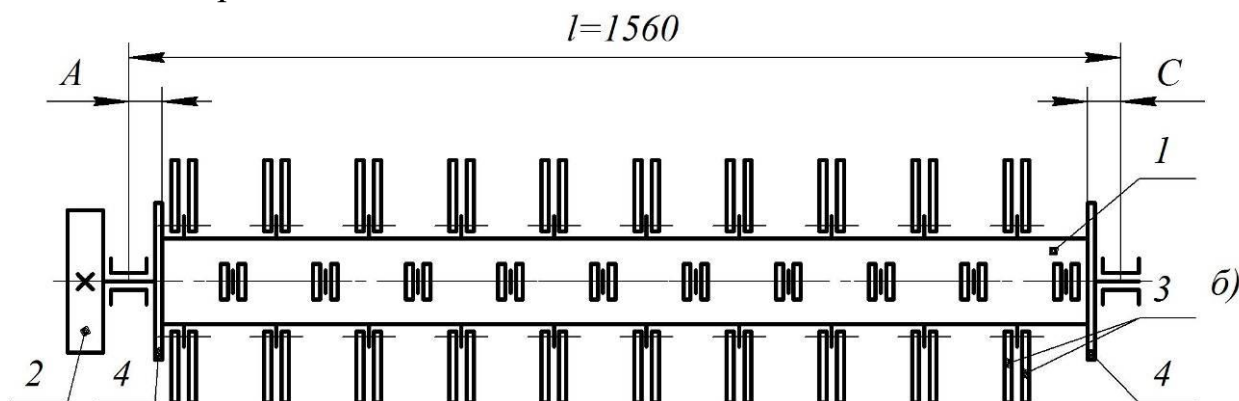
Барабан измельчителя зерноуборочного комбайна «Acros-530»
